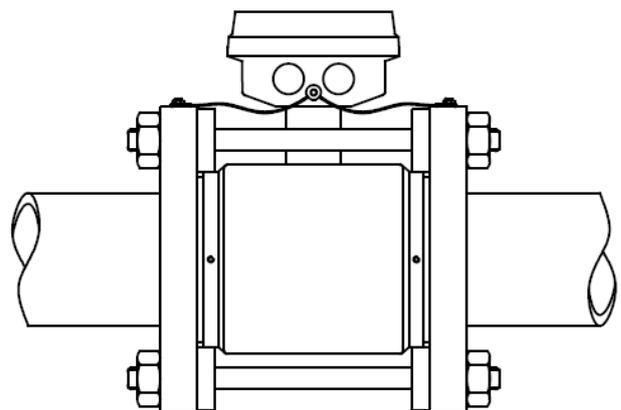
Medidor Waffer, aterrado em tubulação condutiva com flanges soldados.
